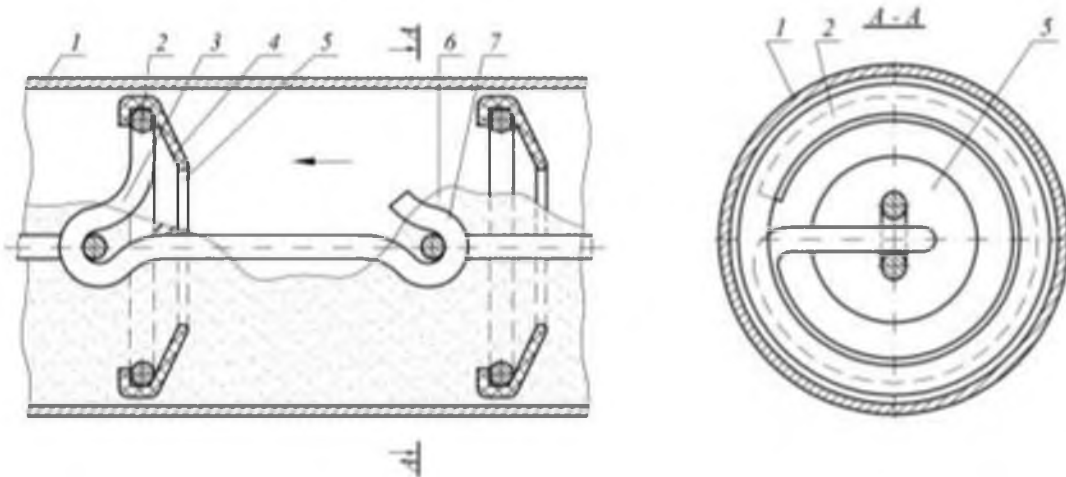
Робочий орган скребкового транспортера-змішувача
